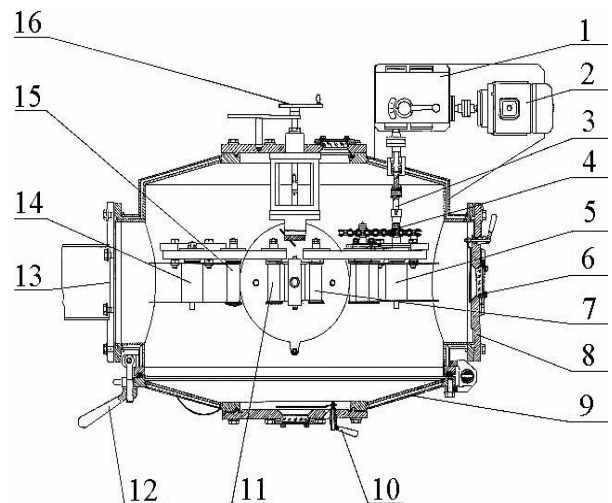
Схема установки (вид сверху): 1 – редуктор; 2 – электродвигатель типа АОЛ-012/4; 3 – ось редуктора; 4 – цепь, приводящая в движение тянущий механизм; 5 – приемная катушка с залуженной лентой; 6 – смотровое окно; 7 – направляющий ролик; 8 – боковой фланец; 9 – корпус верхней части рабочей камеры; 10 – ручка защитного экрана смотрового окна; 11 – направляющий ролик; 12 – болт для закрывания откидной крышки верхней части рабочей камеры; 13 – фланец для подсоединения к вакуумной системе; 14 – подающая катушка с ниобиевой лентой; 15 – направляющий ролик; 16 – механизм опускания штока
